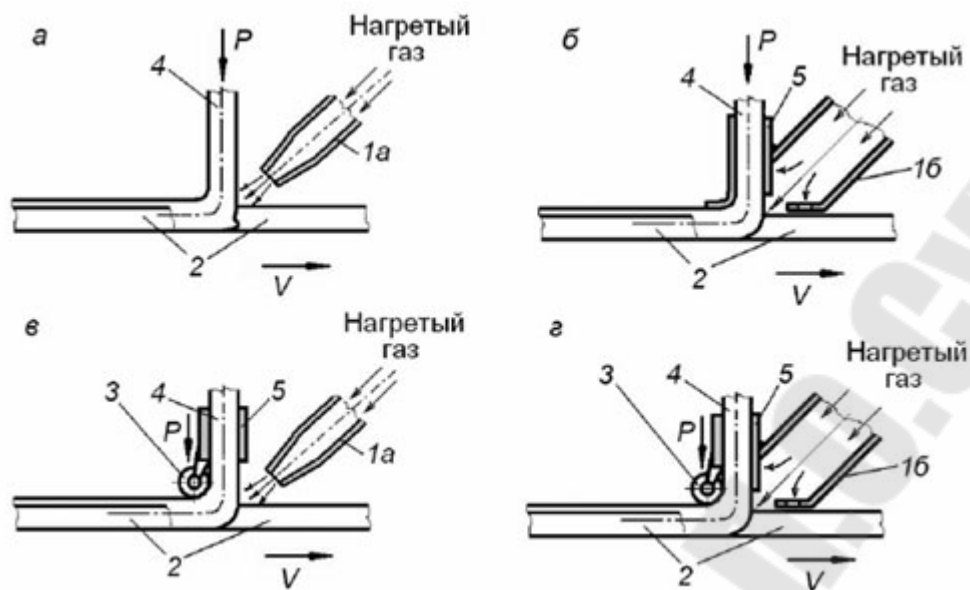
Схемы сварки пластмасс присадочным прутом:
